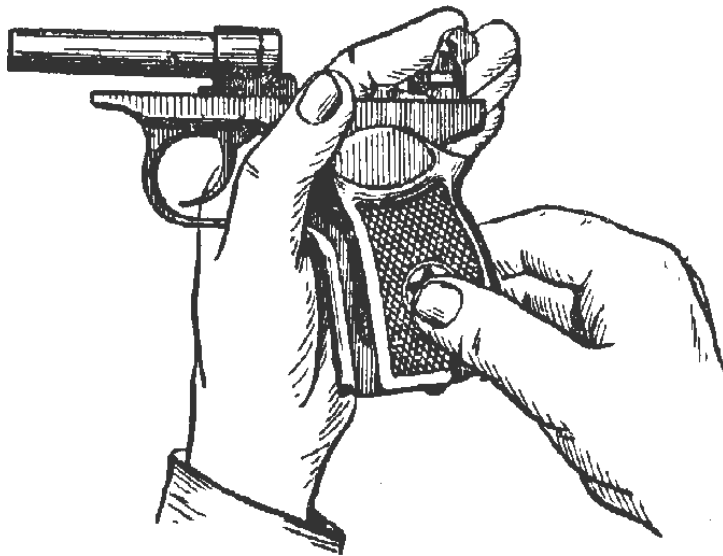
Зняття гачка пружини шептала із затворної затримки
